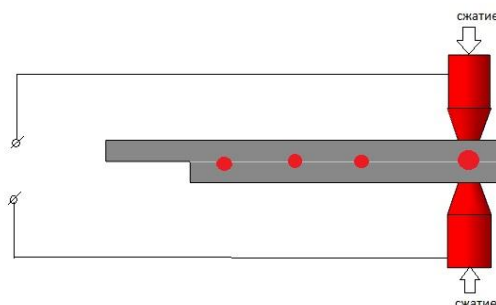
Схема соединения двух однородных металлов путем точечной контактной сварки
